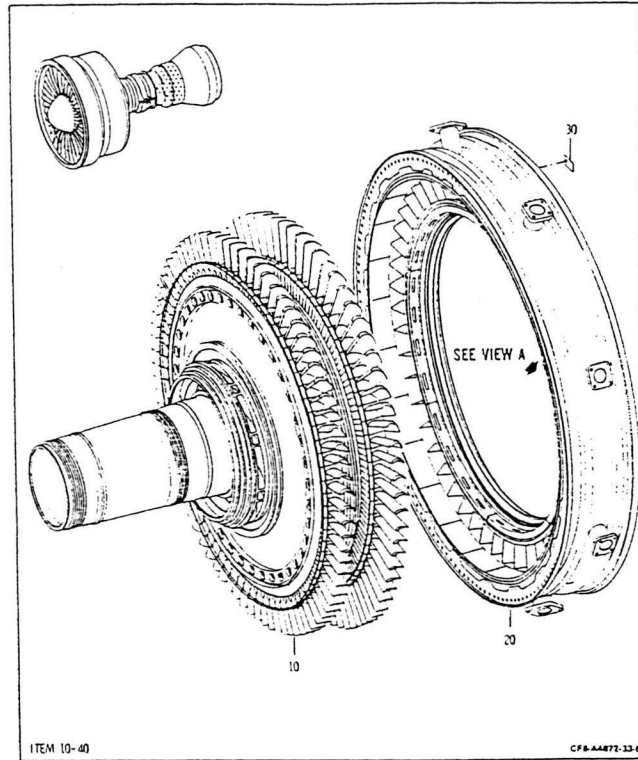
แสดงภาพ 3 B Module (Compressor Rear Frame Assembly)
